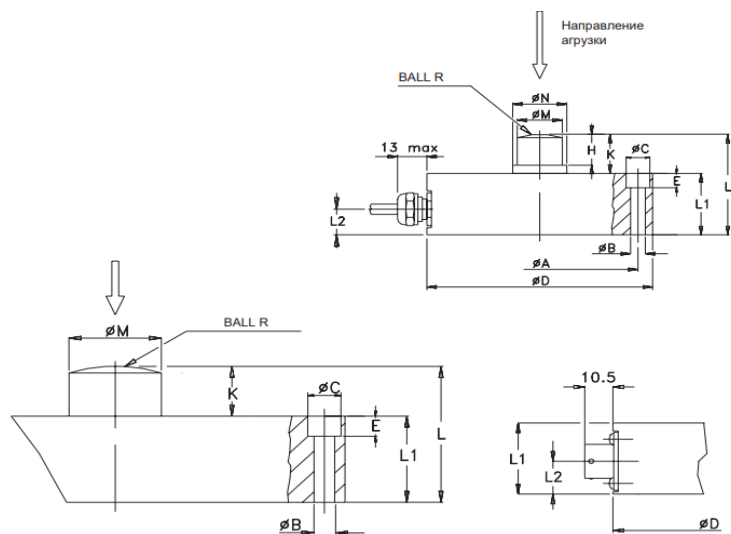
Габаритные и присоединительные размеры тензометрического датчика Gefran CM K2C
